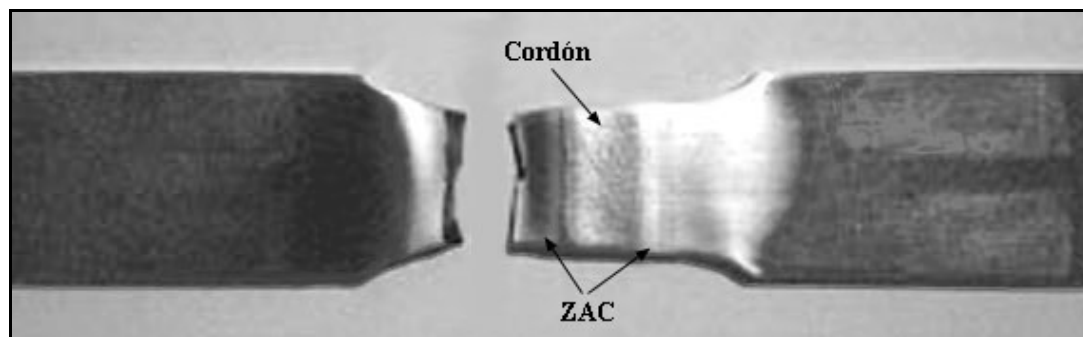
Vista de la fractura de la probeta de tracción de la junta soldada.
